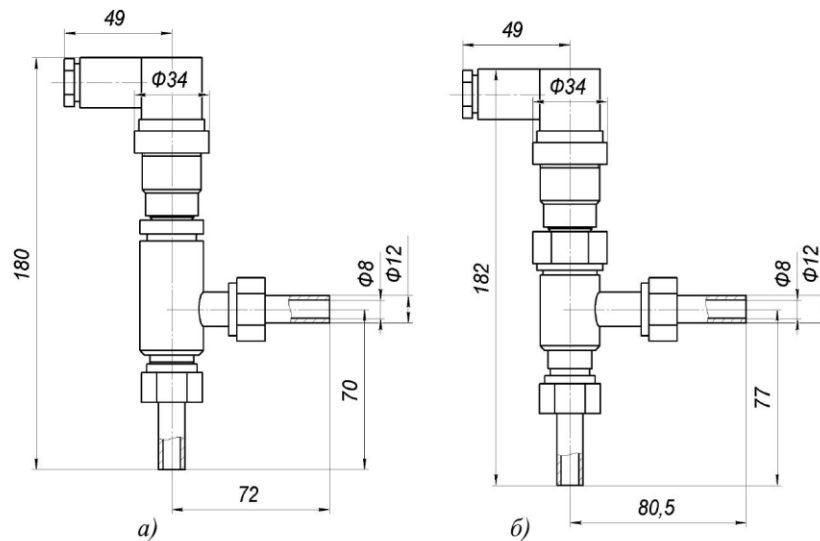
Габаритные и монтажные размеры проточного пассивного датчика ECS-1.15 (0..1000мСм/см) (а); ECS1.16 (0..1000мкСм/см) (б)
